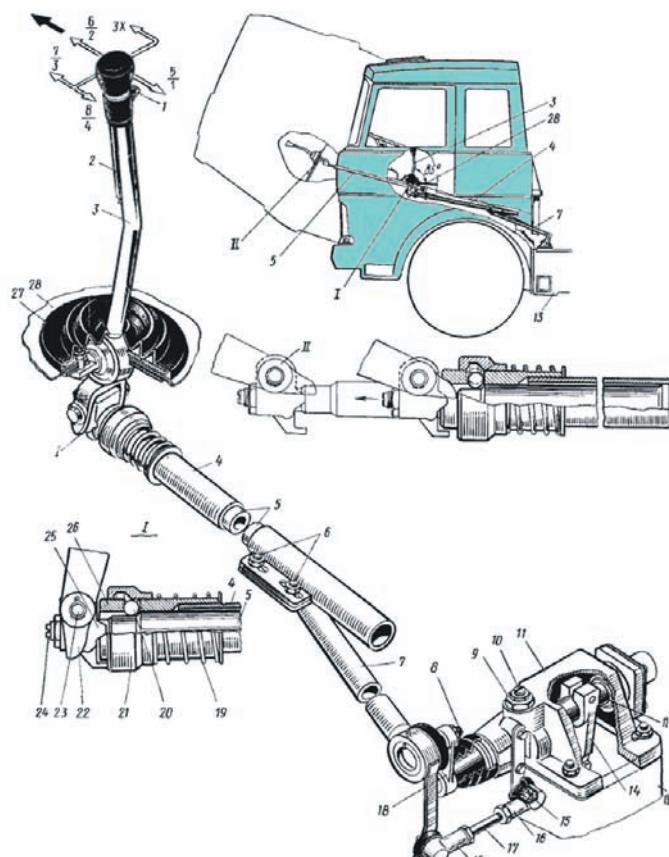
Привод переключения коробки передач: 1 — переключатель диапазонов; 2 — трос управления пневмокраном; 3 — рычаг; 4, 7, 17 — тяги; 6 — болт 8 — шаровой палец; 9 — фиксатор передач; 10 — стопор; 11 — картер; 12 — валик; 13 — основная коробка передач; 14, 18 — рычаги; 15 — шаровой палец; 16 — наконечник; 19 — пружина; 20 — шарик блокировочного устройства; 21 — блокировочная втулка; 22 — вилка; 23 — палец; 24 — хвостовик; 25 — серьга; 26 — наконечник тяги; 27 — уплотнительный чехол; 28 — пол кабины; I — привод в транспортном положении; II - привод при опрокинутой кабине
